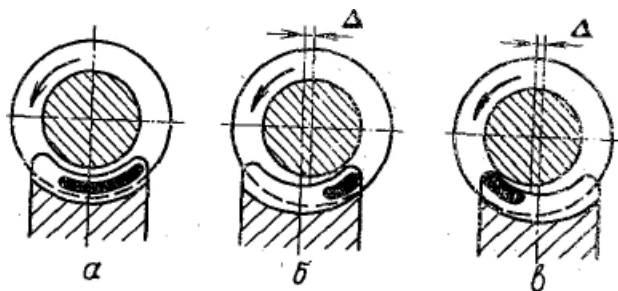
Перевірка установки черв'яка відносно черв'ячного колеса:
